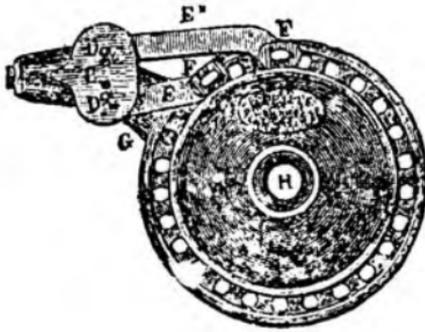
Механизмъ рычажнаго или ударнаго пресса Мабилля.
